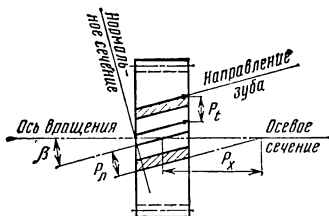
Шаги зацепления косозубого цилиндрического колеса
